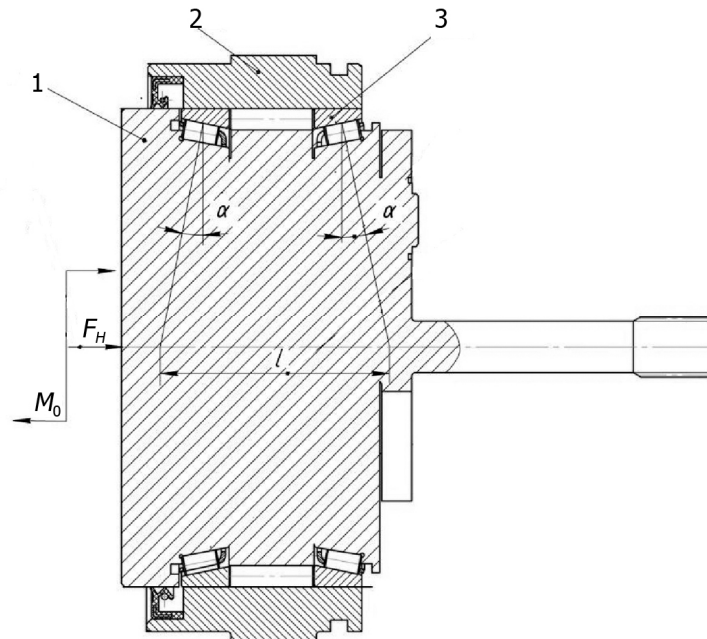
Общая компоновка совмещенных конических опор качения водила планетарно-цевочного редуктора 2К-V: 1 – водило в сборе с комплектующими узлами и деталями; 2 – корпус редуктора; 3 – совмещенная коническая опора качения водила; α – угол контакта конического ролика; M_0 – опрокидывающий момент; F_H – внешняя осевая сила; l – расстояние между точками приложения опорных реакций
